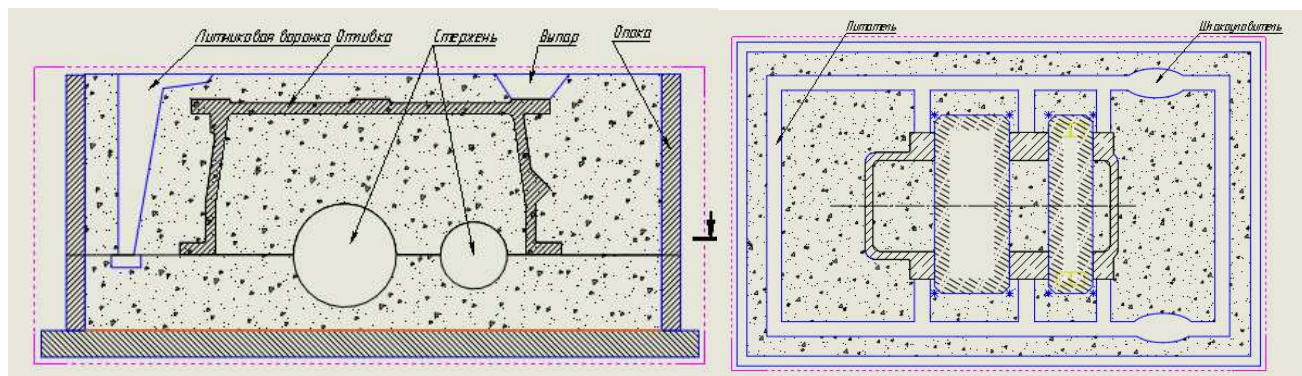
Схема литейной оснастки для изготовления отливки в песчано-глинистой форме
